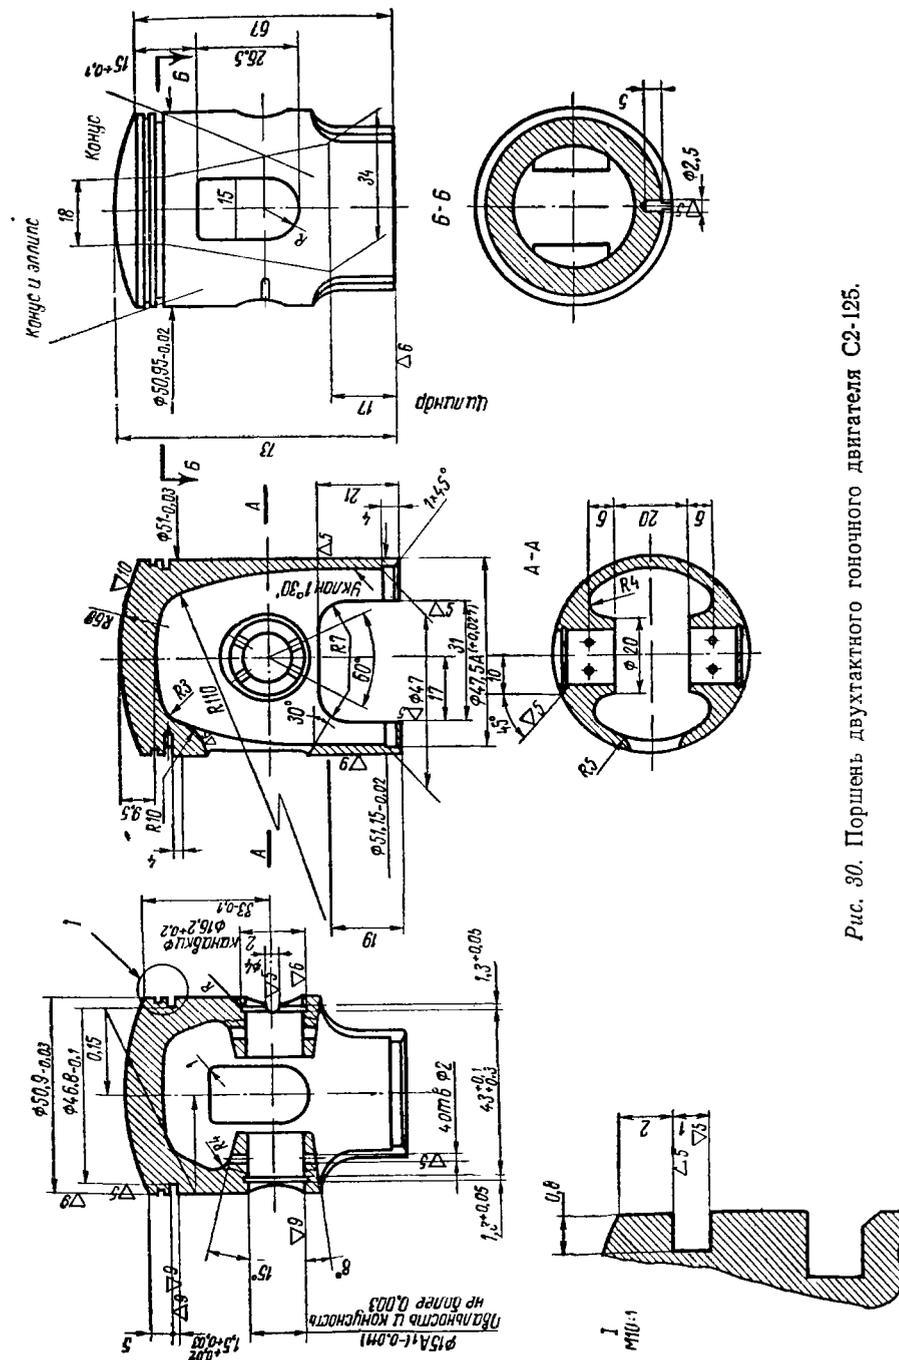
Поршень двухтактного гоночного двигателя С2-125.
